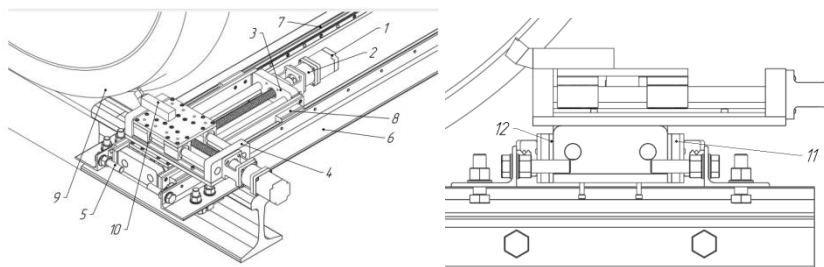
Общий вид станка с ЧПУ для обточки колёсных пар:
